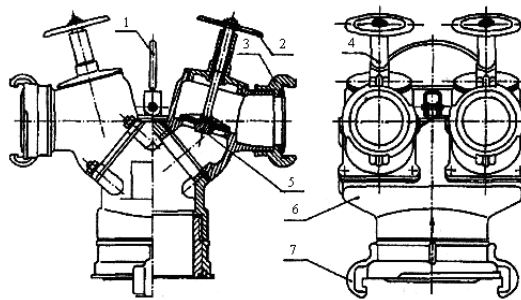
Будова розгалуження рукавного чотирьохходового: 1 — ручка; 2— маховичок; 3 — з'єднувальна головка на вихідному патрубку; 4 — перекриваючий пристрій; 5 — затворний клапан; 6 — корпус; 7 — з'єднувальна головка на вхідному патрубку
